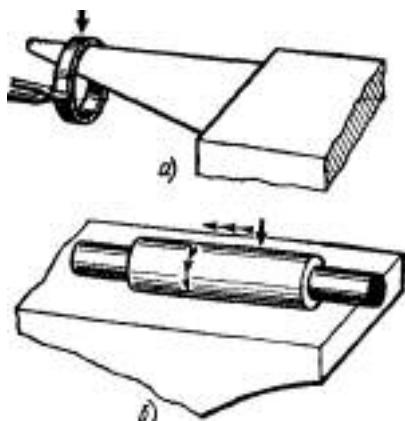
Раскатка заготовок в виде кольца и трубы
